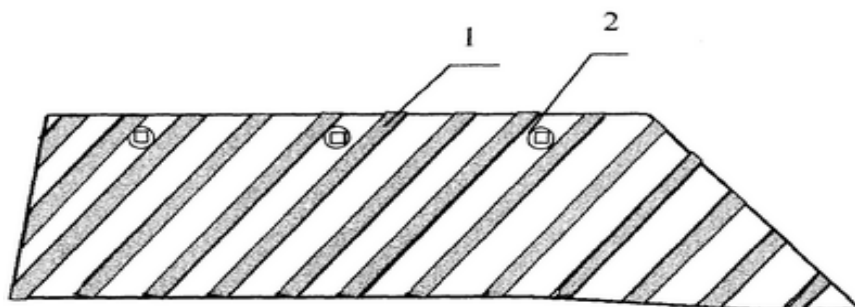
Схема наплавочного армирования рабочей поверхности (на примере цельнометаллического лемеха отечественного производства)
